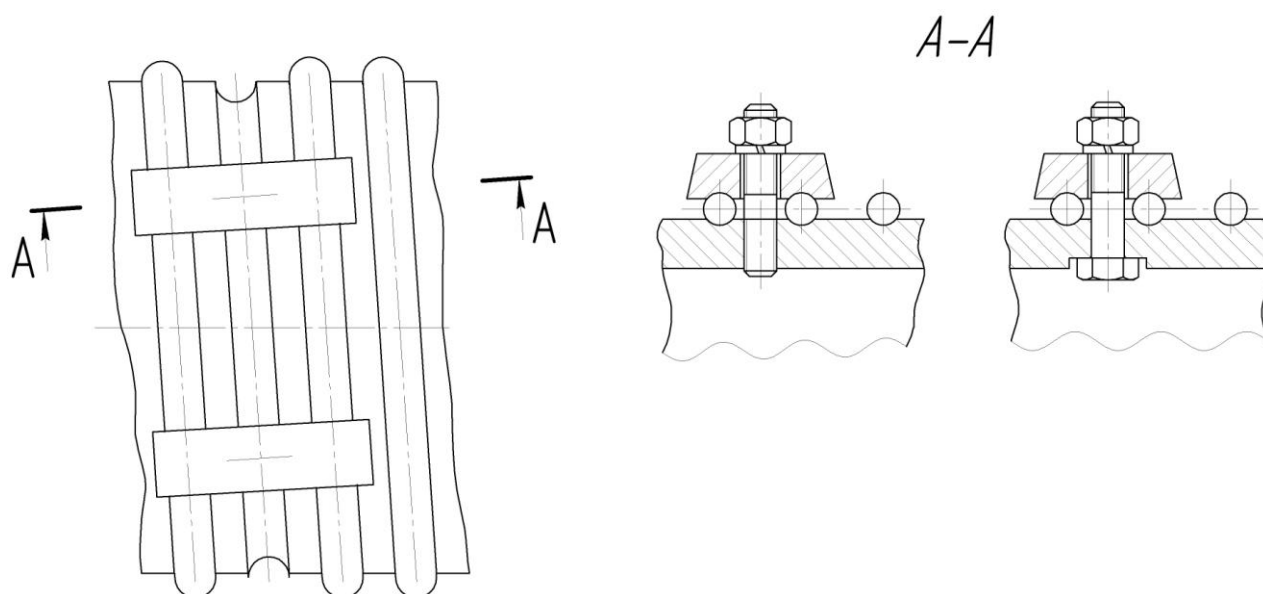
Кріплення каната на барабані: варіанти кріплення накладки шпилькою або болтом і стопоріння пружинною шайбою (А-А)
